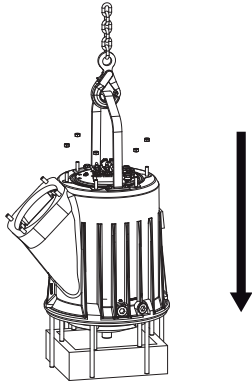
Монтаж охлаждающей рубашки (J 205, J 405)
